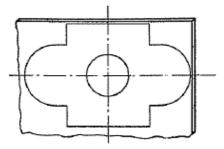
Trazado en el plano (Vidondo y Alvares, 1981, p.94).
